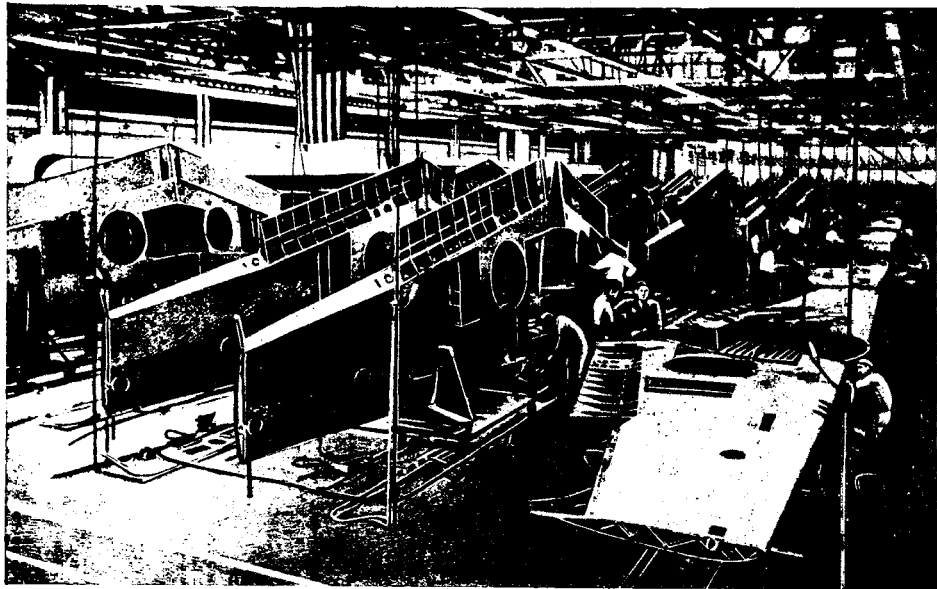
Приспособления для сборки и приклейки дощечек, нервюр и обшивки листовым секциям крыльев
